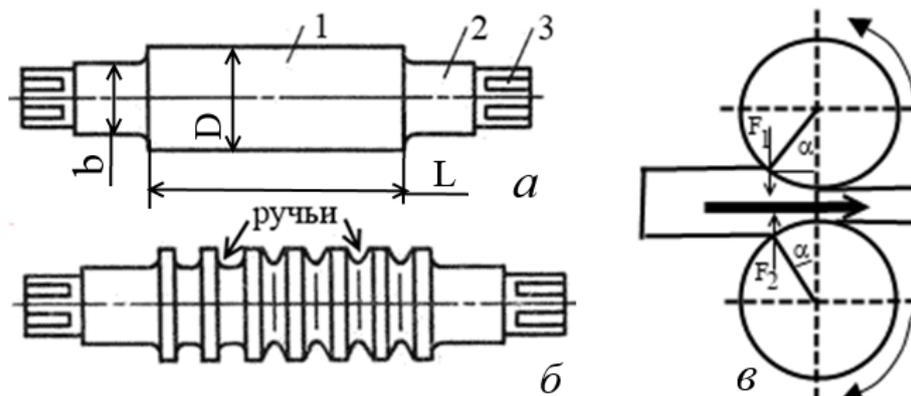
Конструкция валков а, б и схема деформации заготовки при прокатке в.
